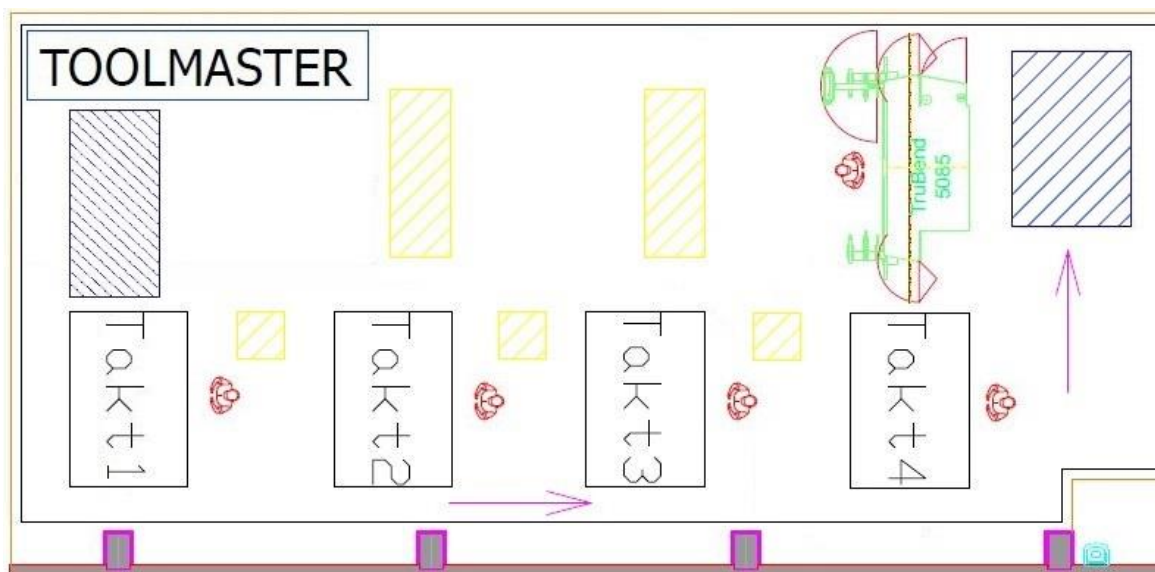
Konečné rozvržení čtyřtaktové montáže ToolMaster
